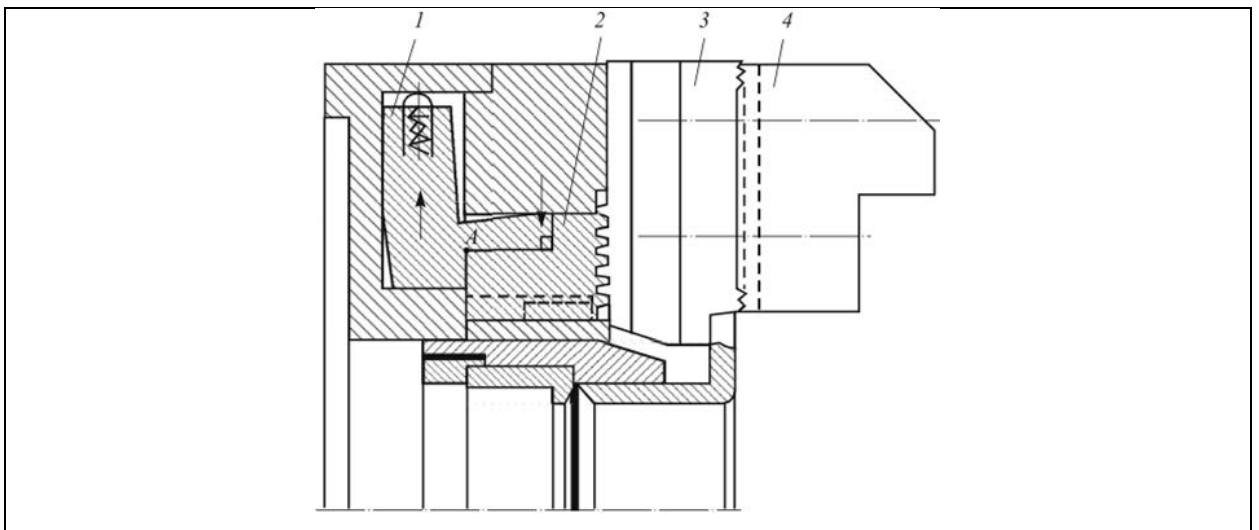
Клинорейковий токарний патрон з компенсатором відцентрової сили
